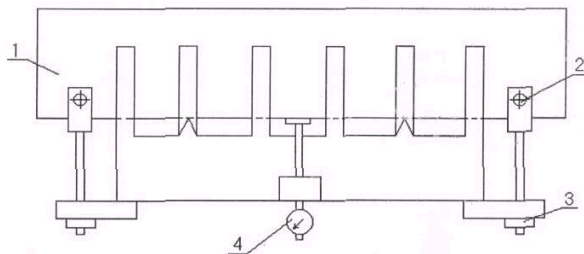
Приспособление для создания предварительного изгиба пластины: 1 – пластина; 2 – штырь; 3 – гайка; 4 – индикатор
